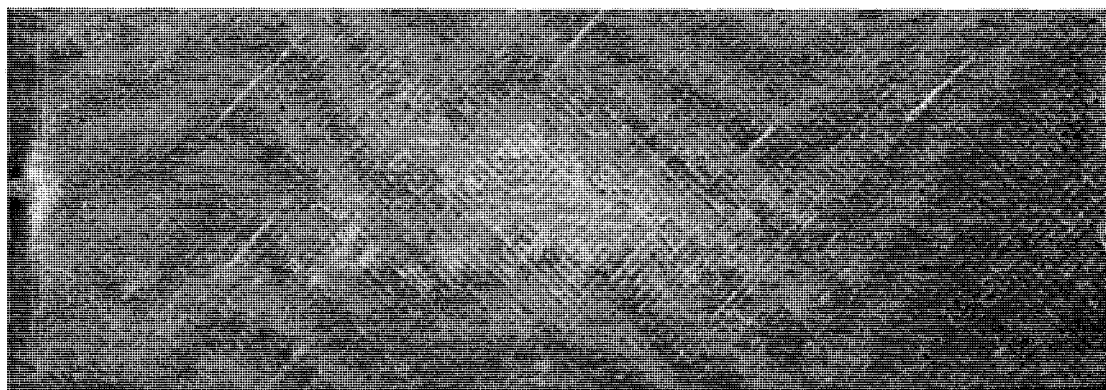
Vue côté moule de la pièce E07PH31 (70g).
